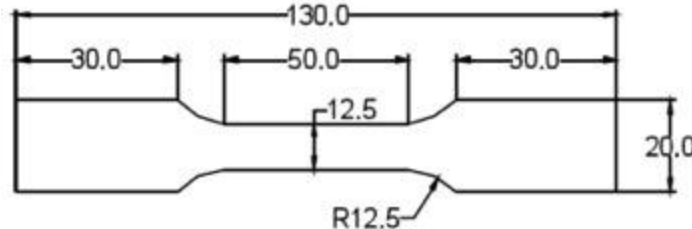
Geometria e dimensões dos provetes do ensaio de tração.
